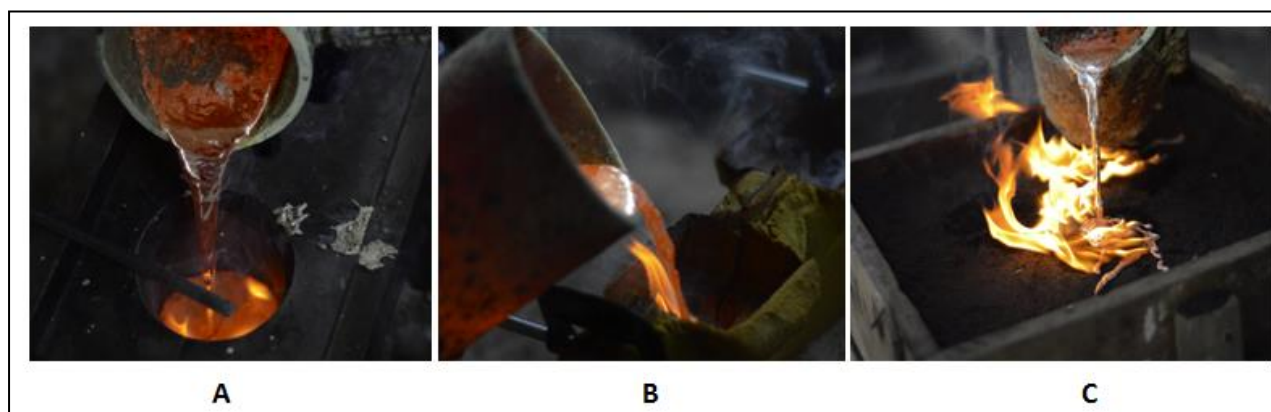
Colado del latón; A) Molde permanente, B) Molde de cáscara, C) Molde de arena.
